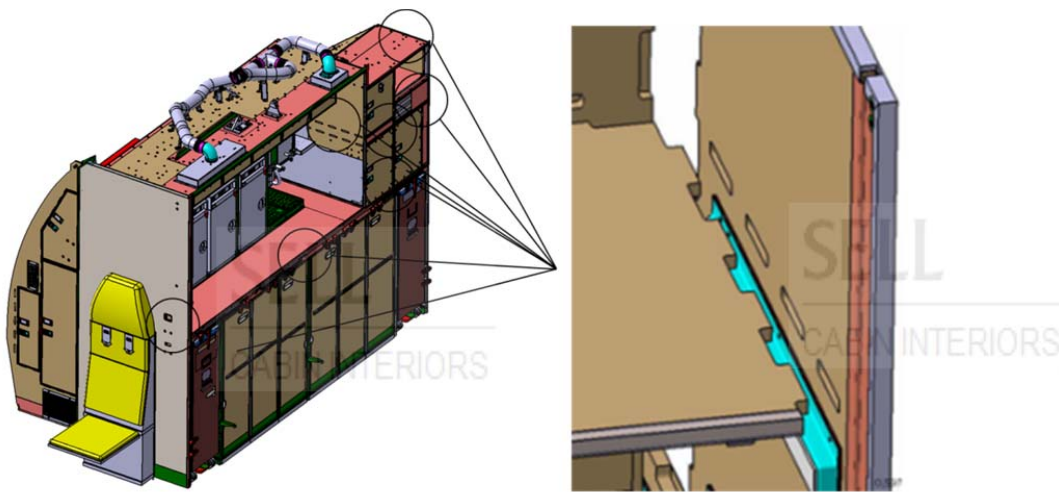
Positionen von unlösbaren Nut-Zapfen-Verbindungen in einer Galley in Sandwichbauweise
